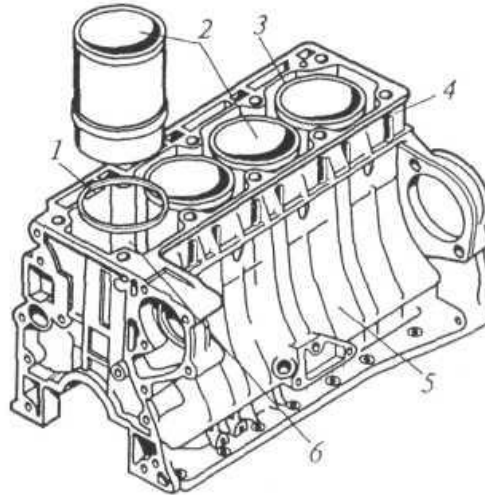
Блок двигателя со съемными гильзами цилиндров
